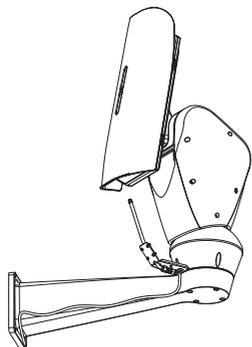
Esempio di installazione del lavavetro alla telecamera PTZ.
